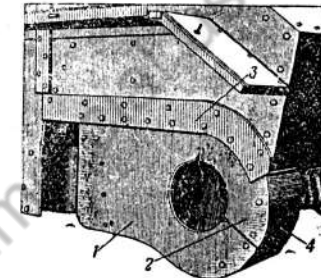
Кормовая часть корпуса: 1 и 2 — броневые листы гитары и бортовой передачи; 3 — накладка; 4 — щиток бортовой передачи
